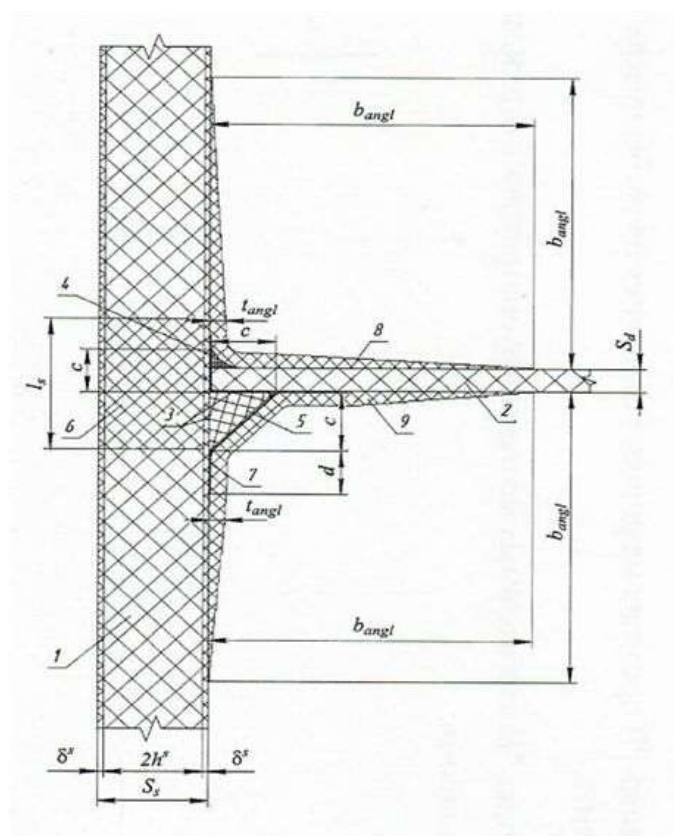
Вузол з'єднання внутрішньої палуби (платформи) одношарової конструкції з обшивкою борту тришарової конструкції: 1 - обшивка борту; 2 - настил внутрішньої палуби (платформи); 3, 4 – адгезійна речовина; 5 - опорний елемент; 6 - посилення з пінопласту підвищеної густини; 7 - обформовка; 8 - верхній приформовочний косинець; 9 - нижній приформовочний косинець
